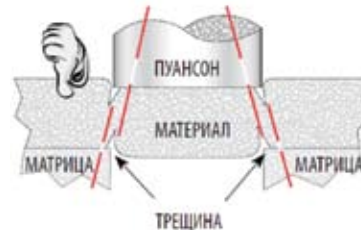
в. Зазор слишком мал – образуются двойная трещина, увеличивается усилие штамповки, снижается срок службы инструмента
